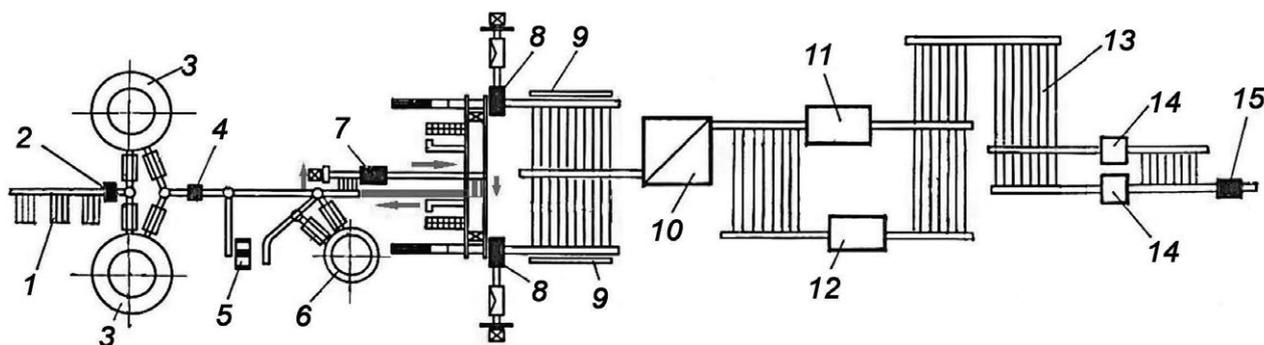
Схема расположения оборудования современного трубопрокатного агрегата с пилигримовым станом ТПА 5-16" при осуществлении «прямой» прошивки заготовки (обозначения аналогичны рис. 1)
